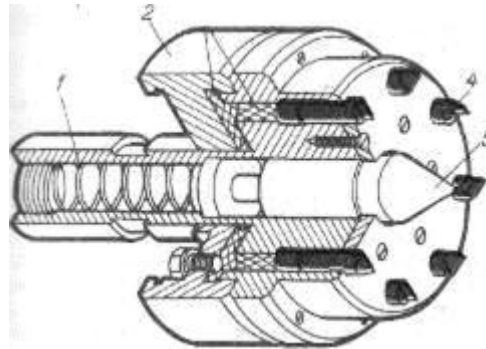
Повідковий патрон з плаваючими ножами: 1 - пружина; 2 - корпус; 3 - гідропласт; 4 - ніж упору; 5 – центр
